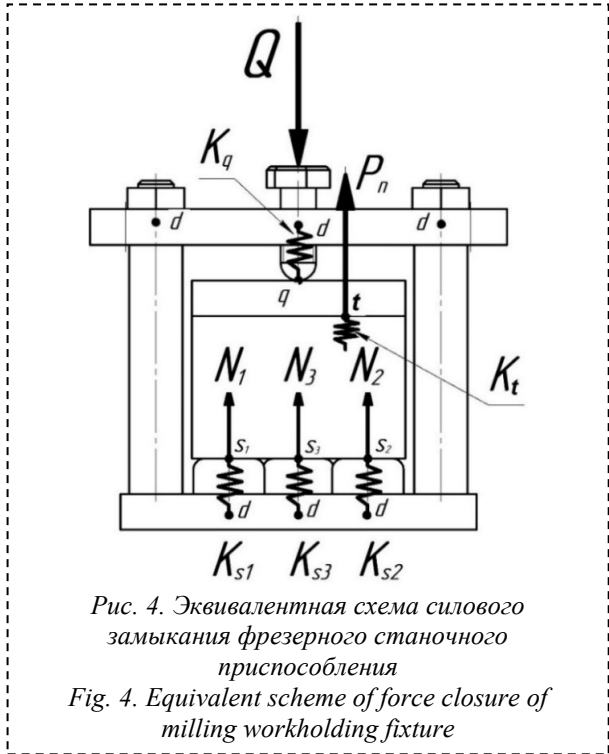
Эквивалентная схема силового замыкания фрезерного станочного приспособления
